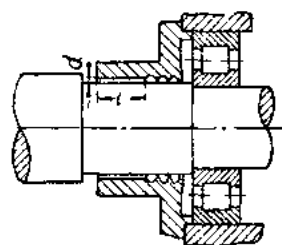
对于电动机和发电机滚珠轴承和滚柱轴承的防爆型密封形式，这种密封，相对于轴承盖有确定的位置
